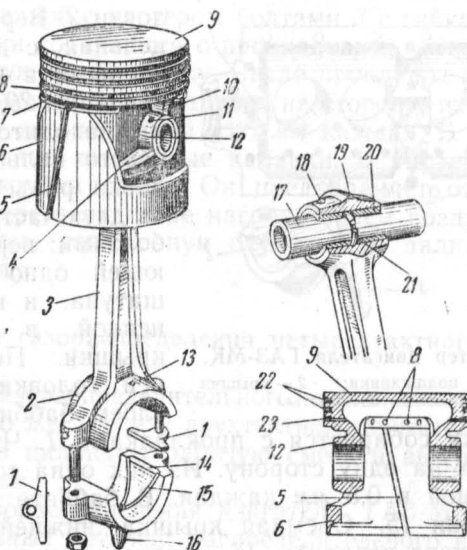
Поршни и шатуны двигателя ГАЗ-МК:
